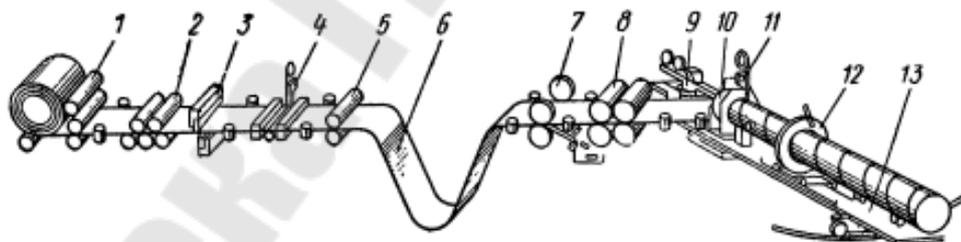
Линия изготовления сварных труб со спиральным швом
